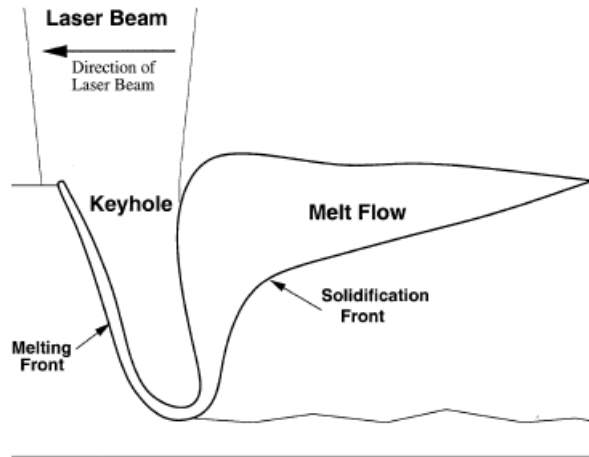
Esquema del proceso de soldadura láser en modo de cráter.
